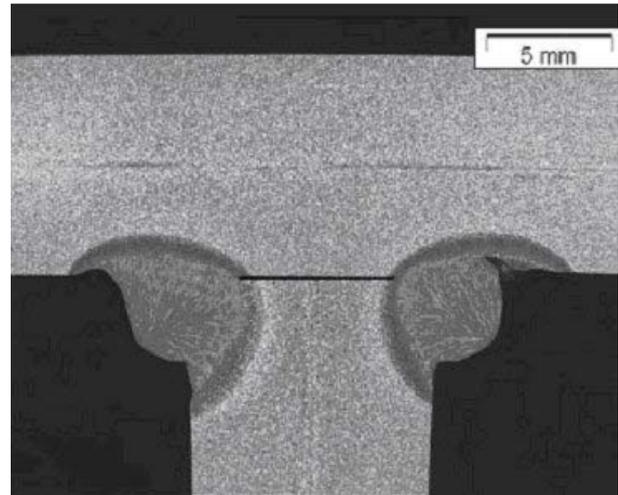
T-Stoß ungenügend durchgeschweißst
